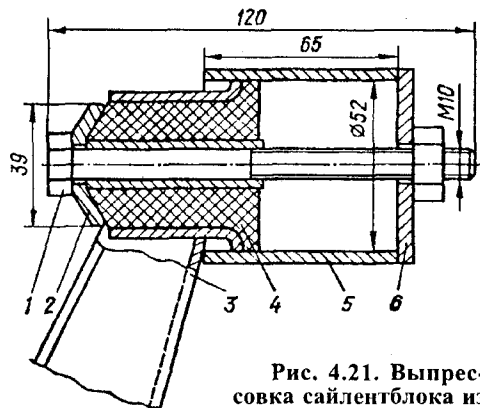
Выпрессовка сайлентблока из рычага балки задней подвески: 1 – болт; 2 – шайба нажимная; 3 – рычаг подвески; 4 – сайлентблок; 5 – втулка опорная; 6 – шайба
